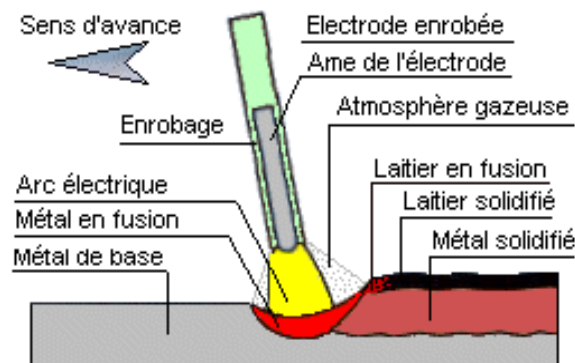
soudage à l'arc à l'électrode enrobée. [5]
